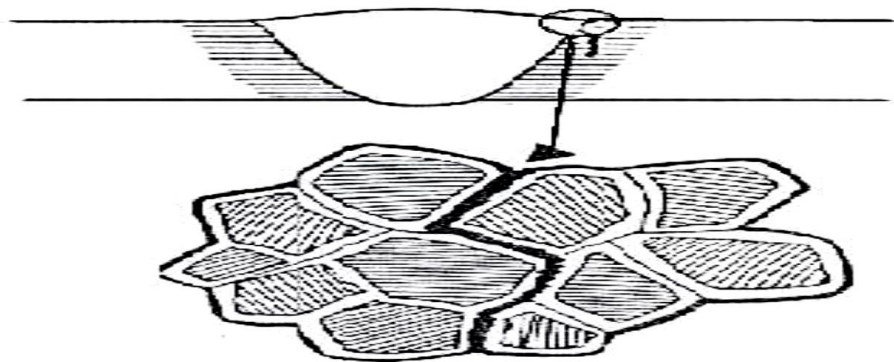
Fissuration du joint de liaison [19].
